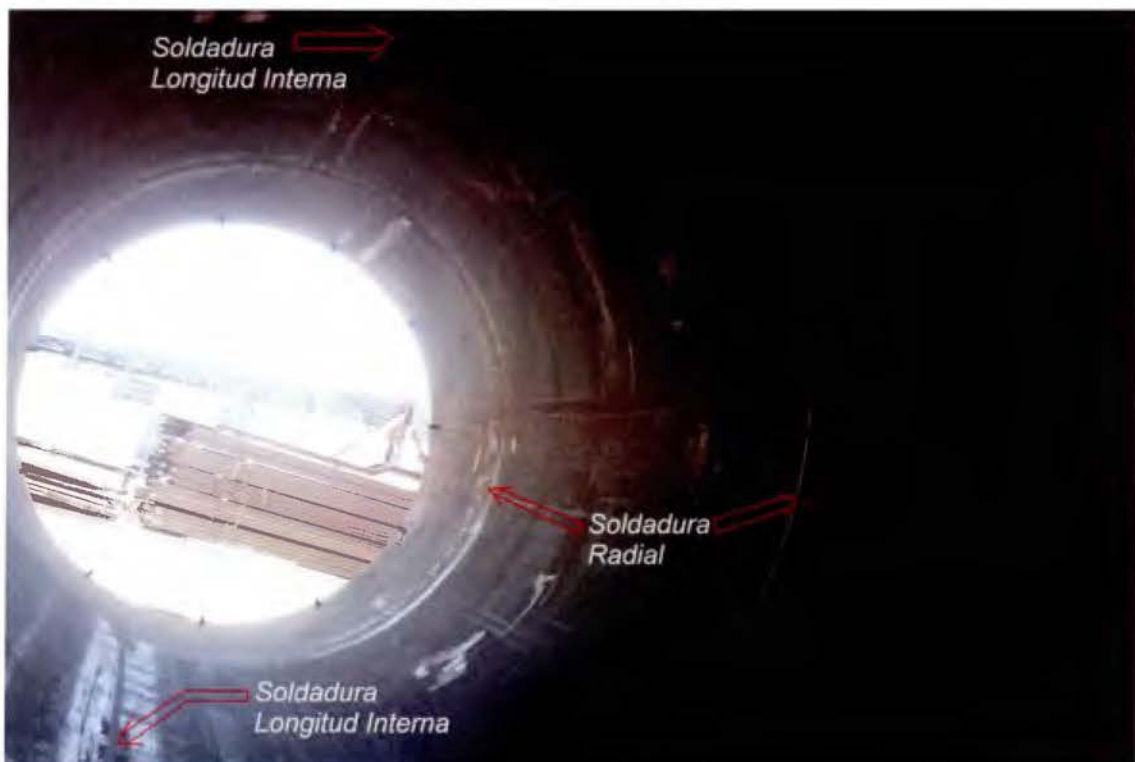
Imagen de tubería soldada en el sitio de trabajo
